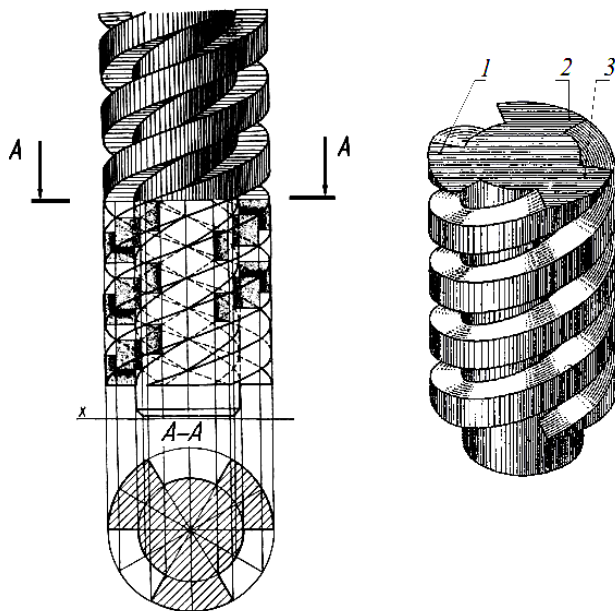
Трехзаходный винт с резьбой прямоугольного профиля
